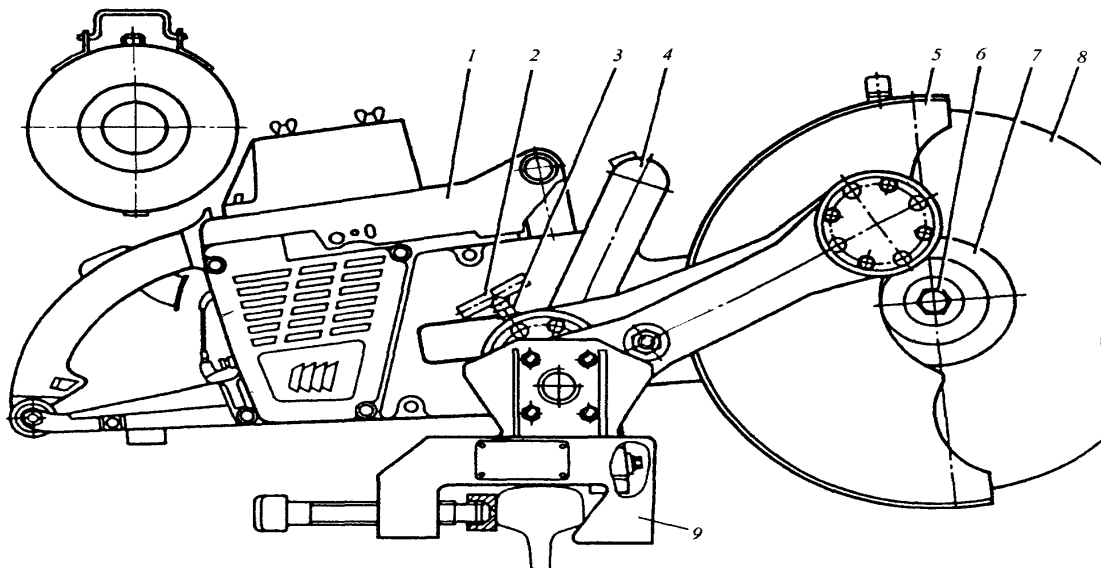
Станок рельсорезный РР80: 1-двигатель; 2-винт; 3-пружина; 4-кронштейн; 5-защитный кожух; 6-болт; 7-нажимная шайба; 8-отрезной круг; 9 – направляющая рама
